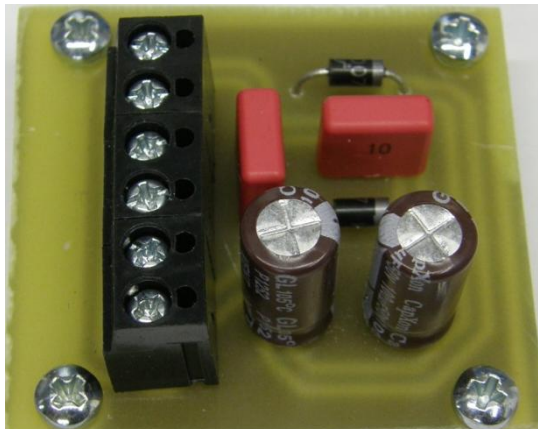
Vytvořená deska pro ovládání motorku pomocí H-můstku
